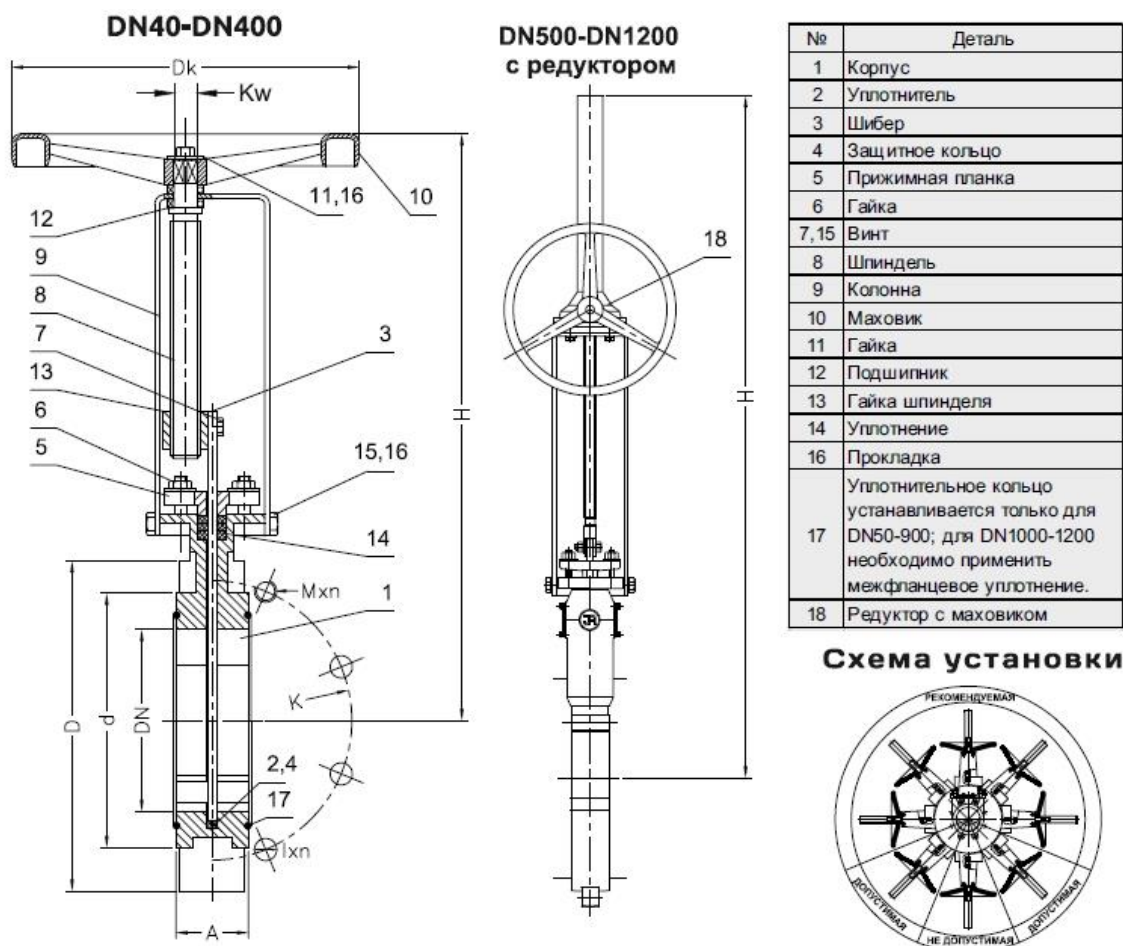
Конструкция задвижки шиберной с редуктором [4]
